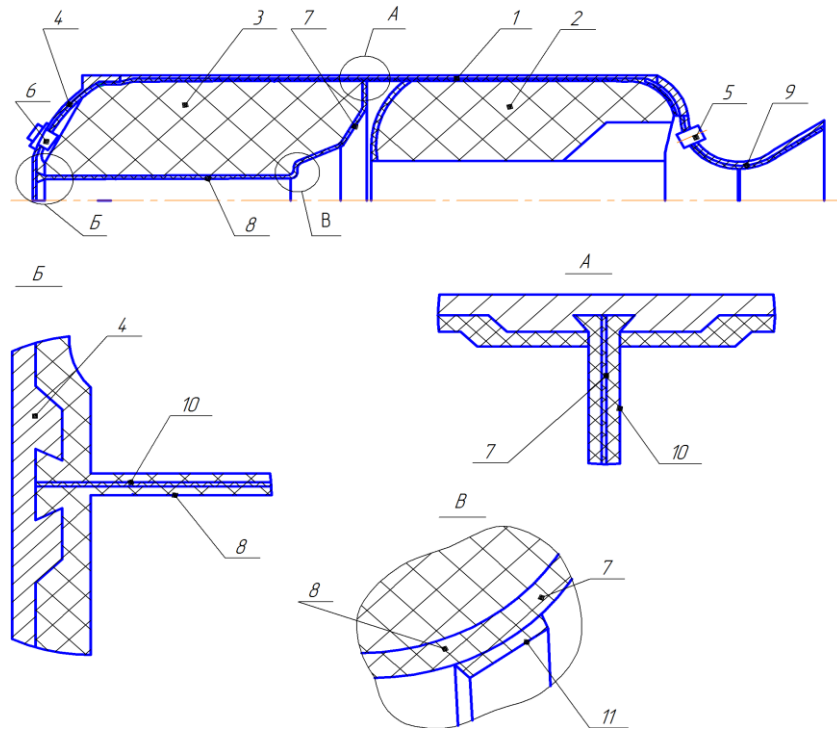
Конструкция двухрежимного ракетного двигателя.
